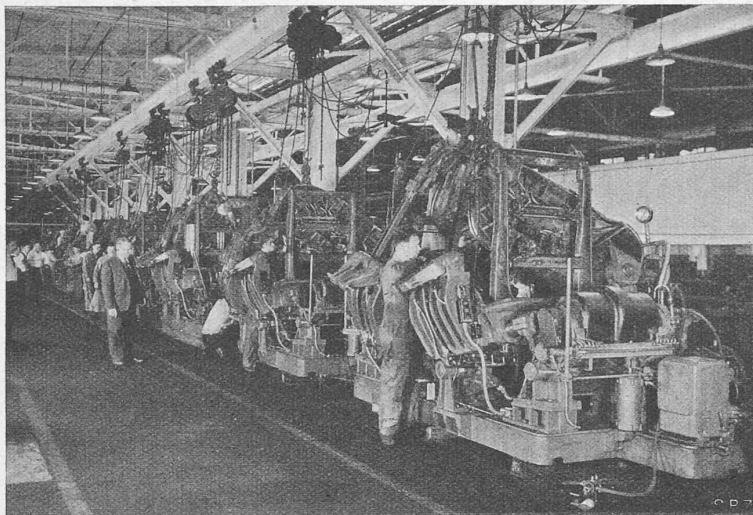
300 kVA-Karosserie-Schweissmaschinen in einer Automobilfabrik
